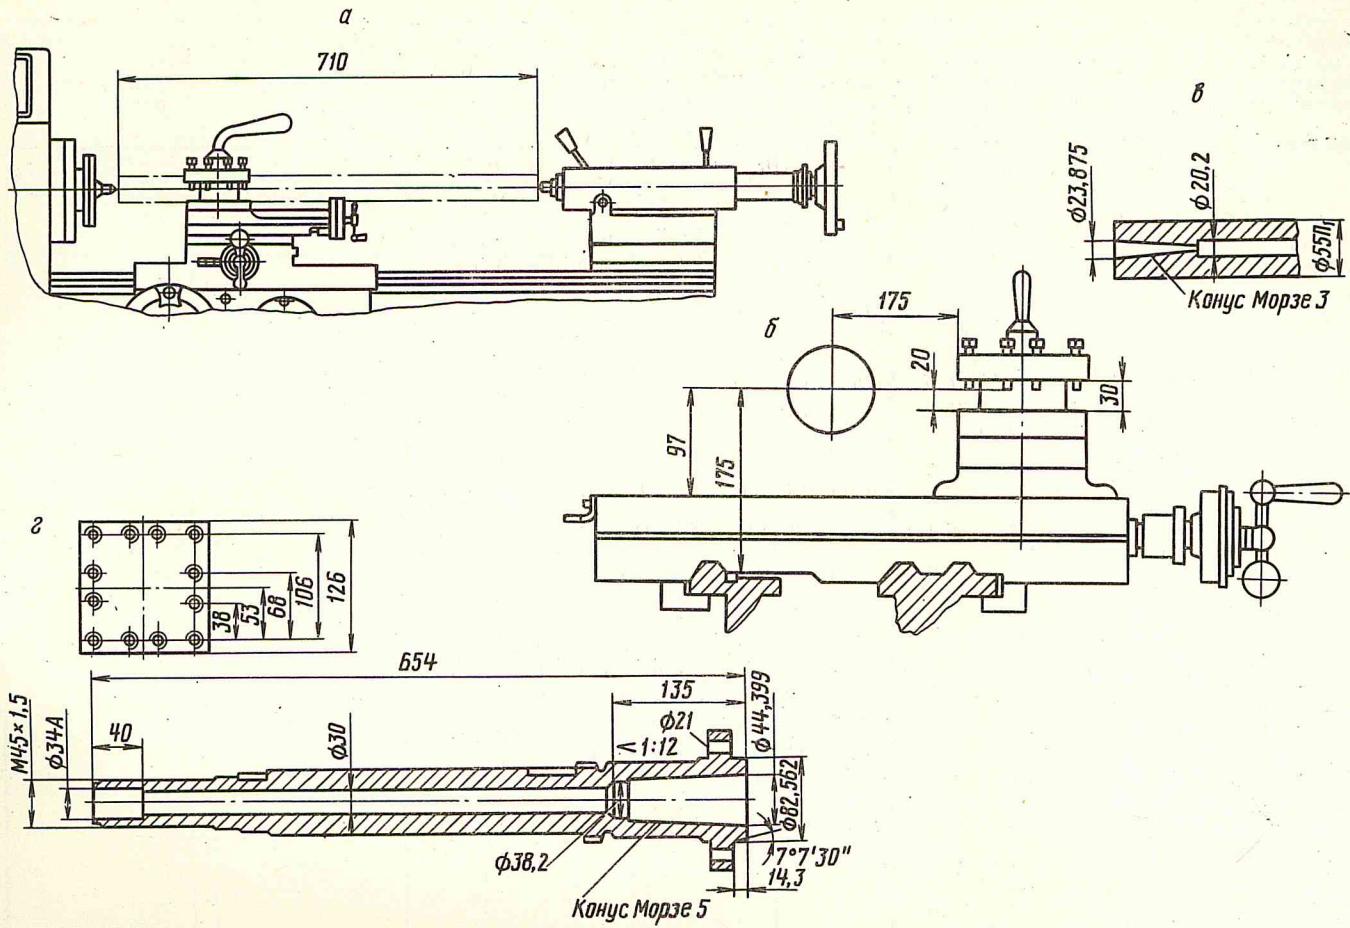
Габарит рабочего пространства; посадочные и присоединительные базы станка:
